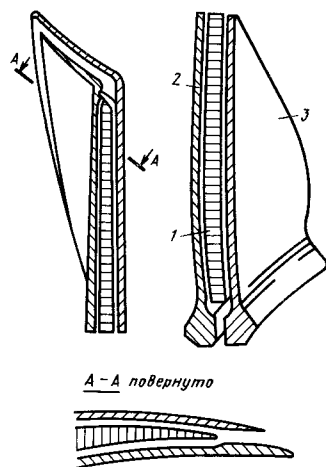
Лопатка вентилятора двигателя RB 211-535E4: 1 — наполнитель сотовой конструкции; 2 — оболочки-обшивки
